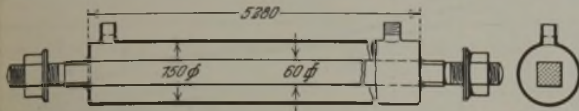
Wassergekühlter Ofenanker alter Ausführung.
